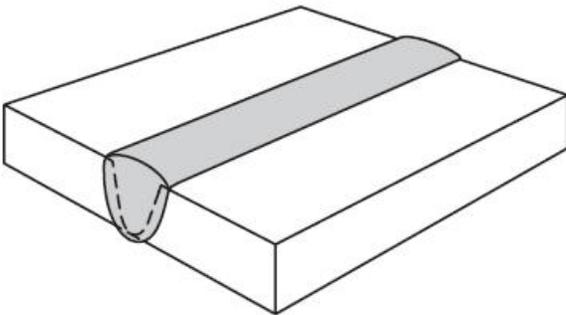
Juntas Soldadas Ranura Simple
